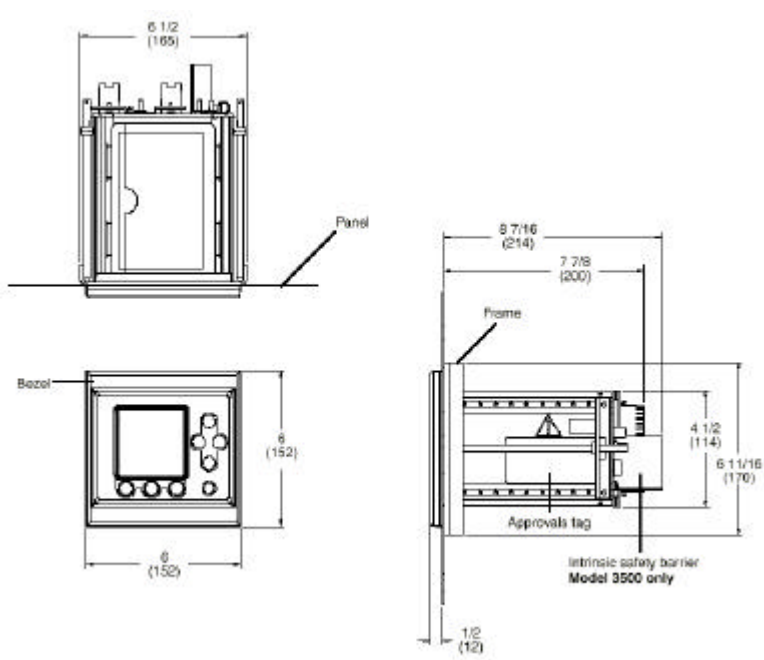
Dimensiones del controlador de Batch Discreto 3300.
